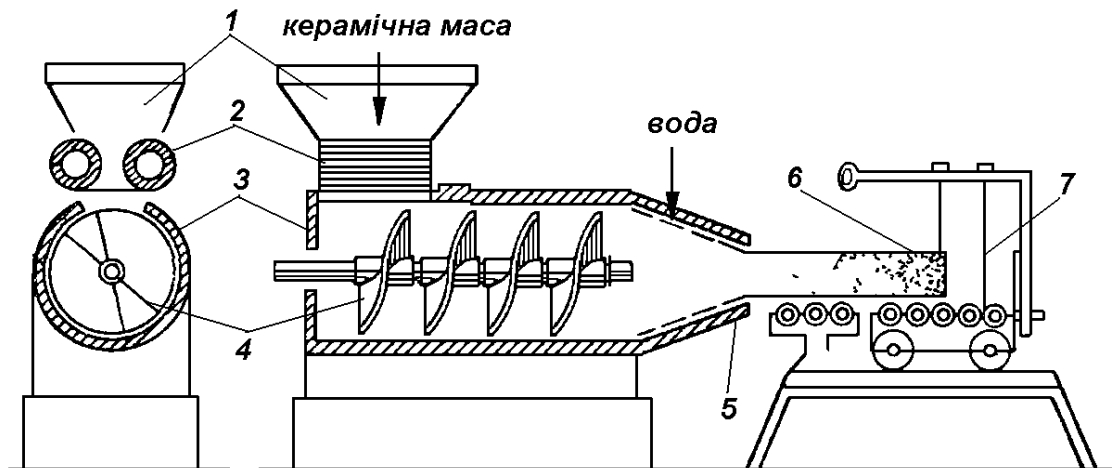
Формувальний прес: 1 – завантажувальна коробочка; 2 – вальці для подавання керамічної маси; 3 – пресувальний барабан; 4 – шнек; 5 – мундштук; 6 – спресована керамічна маса; 7 – пристрій для розрізання маси.
